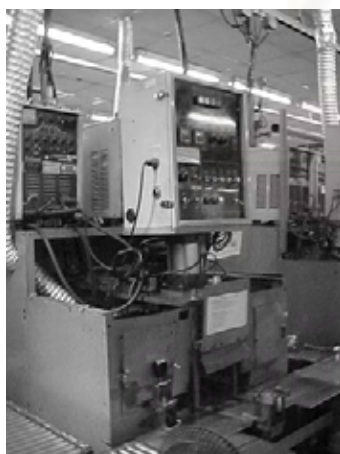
เครื่อง Joint welding
